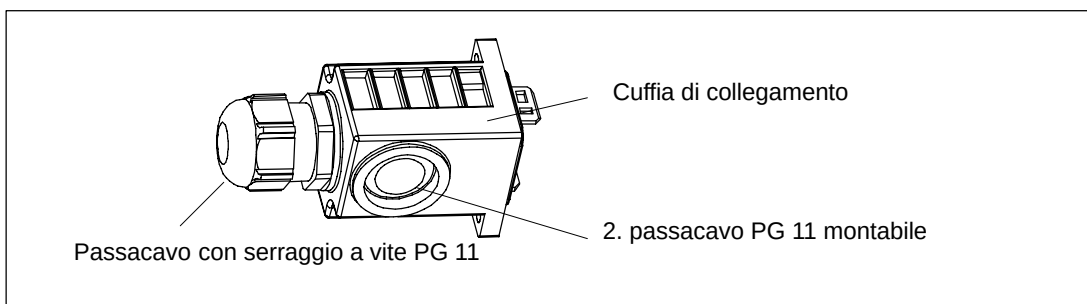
Spina di collegamento: cuffia di collegamento con un passacavo PG
